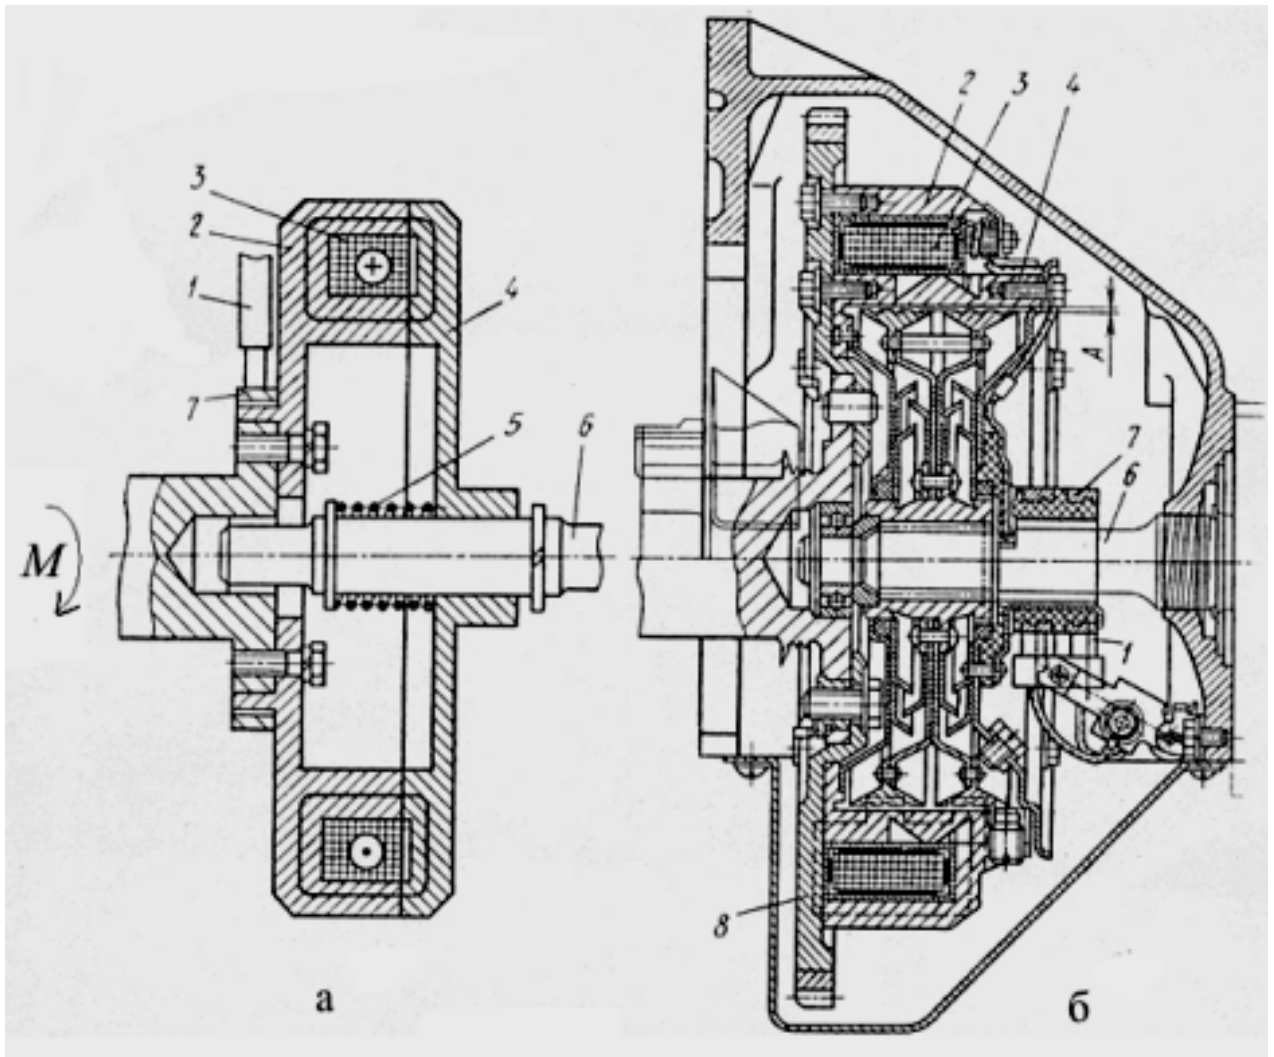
Электромагнитное сцепления: а - без ферронаполнителя, б - с ферронаполнелем; 1 - щетки; 2 сердечник; 3 - обмотка; 4 - якорь; 5 - пружина; 6 - вал сцепления; 7 - кольцо; 8 - маховик
